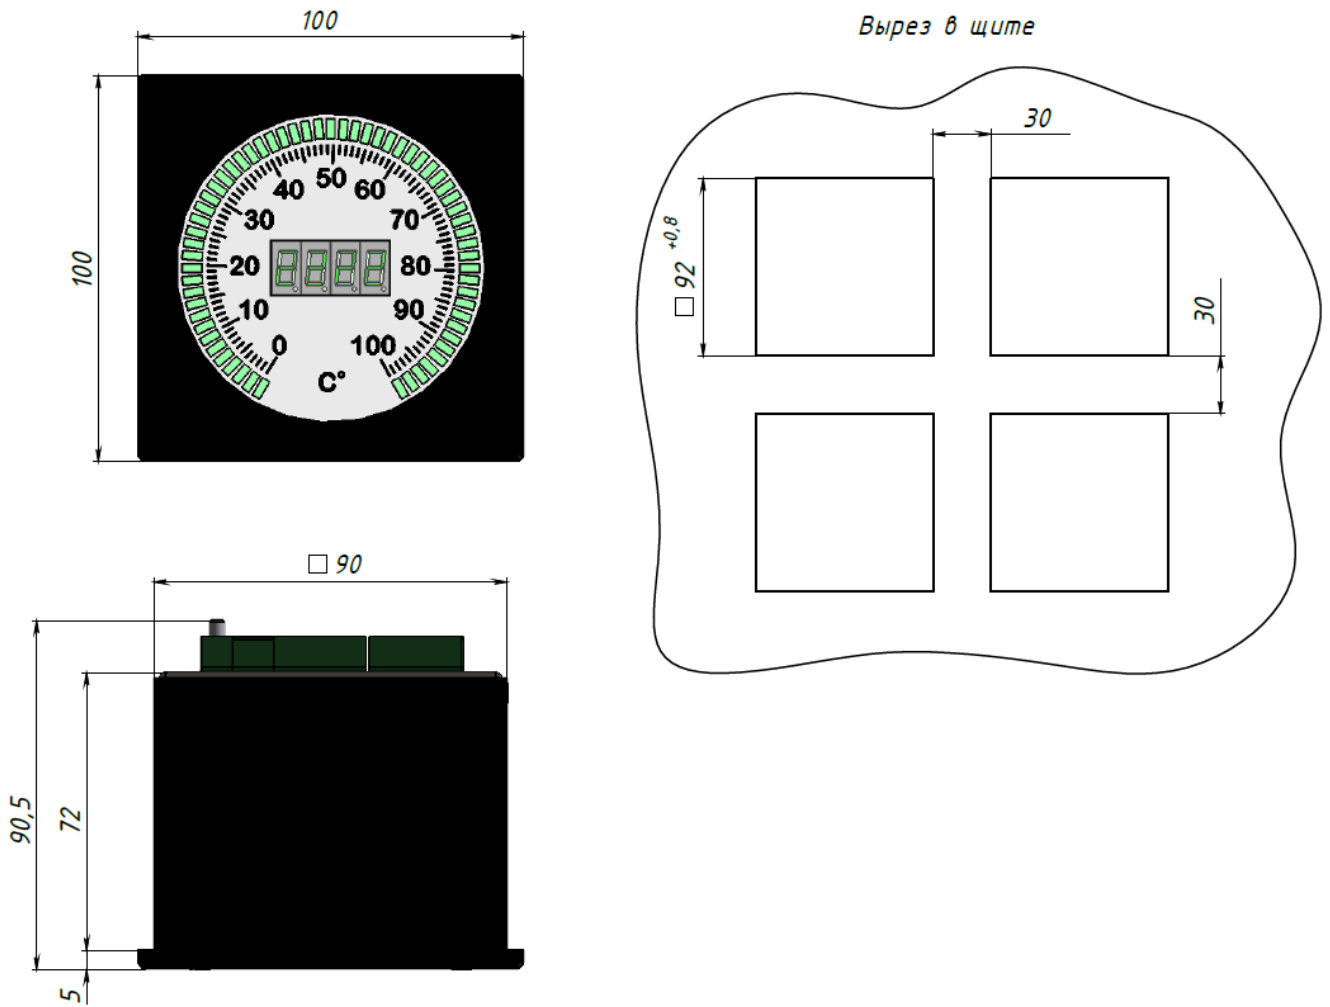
Габаритные размеры прибора Ш932.1К2
